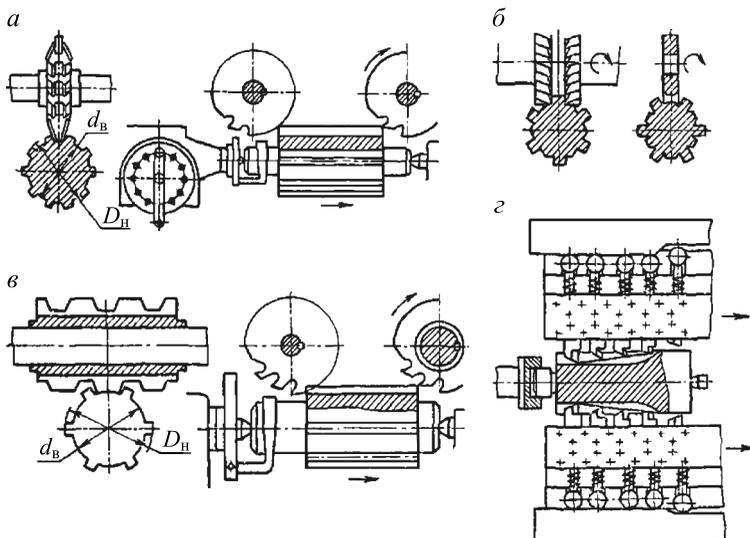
Схемы фрезерования и протягивания шлицев валов
